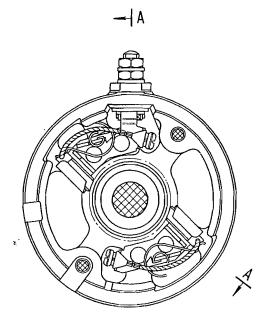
Sezione trasversale e vista del supporto lato collettore.
